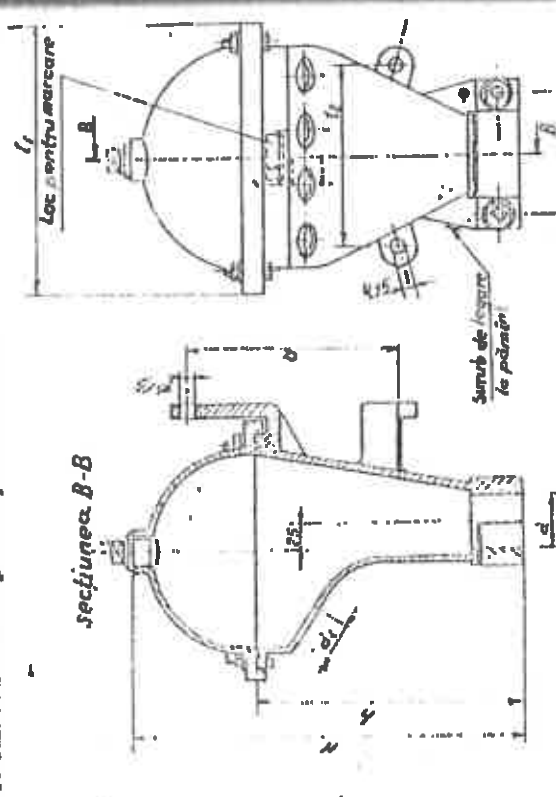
Cutie terminală pentru montaj pe stîlp.
